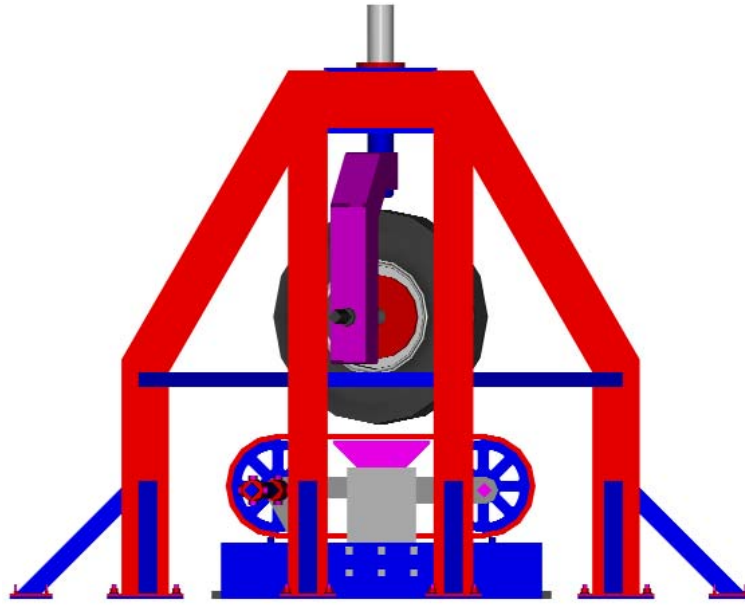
Vista posterior del banco llanta con dirección de 20°
